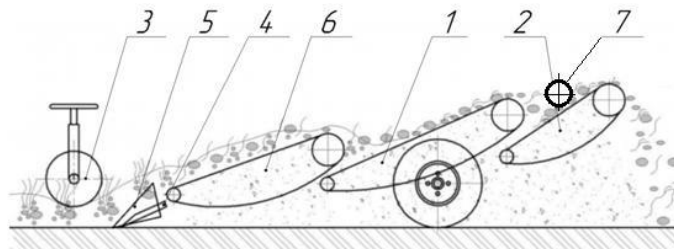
Конструктивно-технологічна схема модернізованого картоплекопача КСТ-1,4: 1 – додатковий сепаруючий елеватор; 2 – каскадний сепаруючий елеватор; 3 – копіювальний каток; 4 – леміш; 5 – ніж; 6 – основний сепаруючий елеватор; 7 – поперечний зворушувач.
